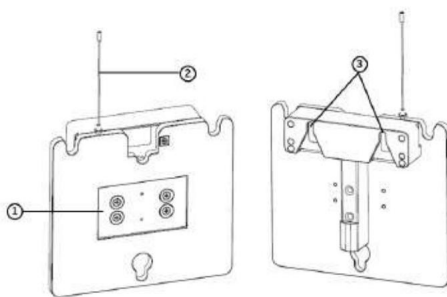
Placa de montaje AUTEL-CSC050A/17
